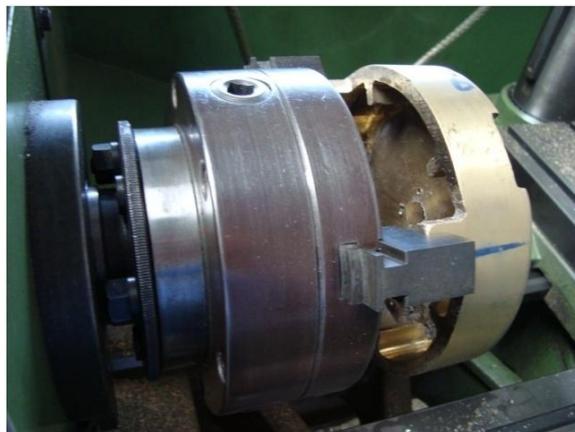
Montaje de la pieza a realizar el orificio para el torquimetro
